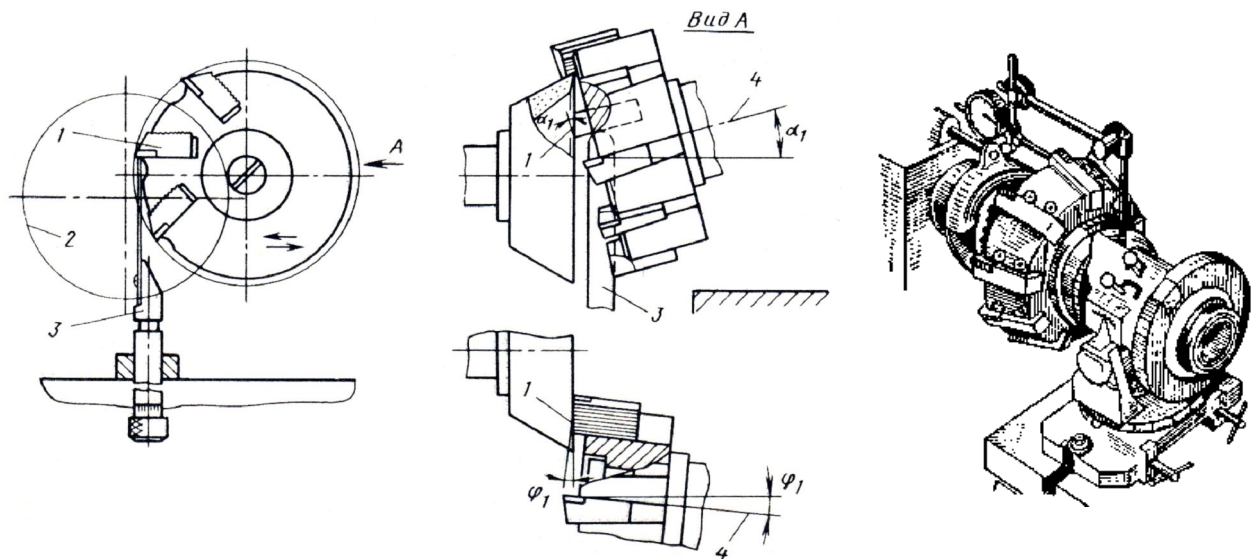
Пристосування для заточення торцевих фрез:
